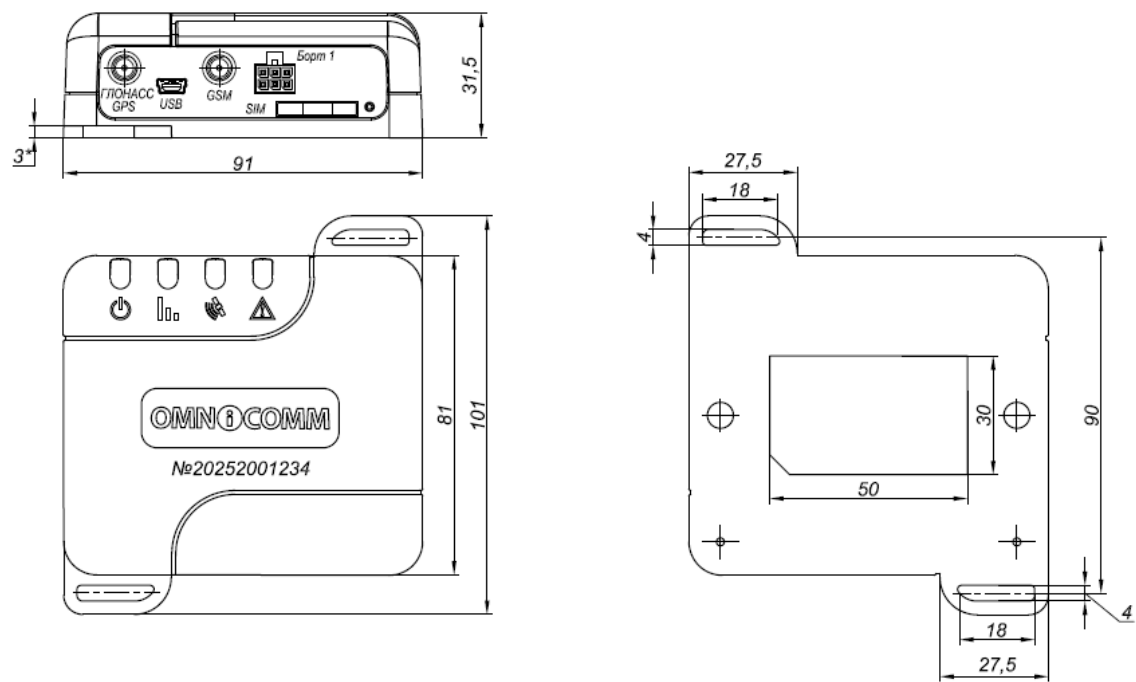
Габаритный чертеж Терминала Omnicomm Smart
